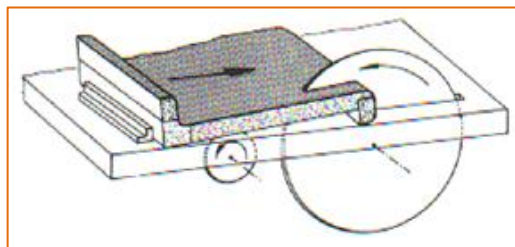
Fertigschnitt an einem Z-förmigen Verbundelement mit einem Hauptsägeblatt großen Durchmessers und Ritzsäge.
